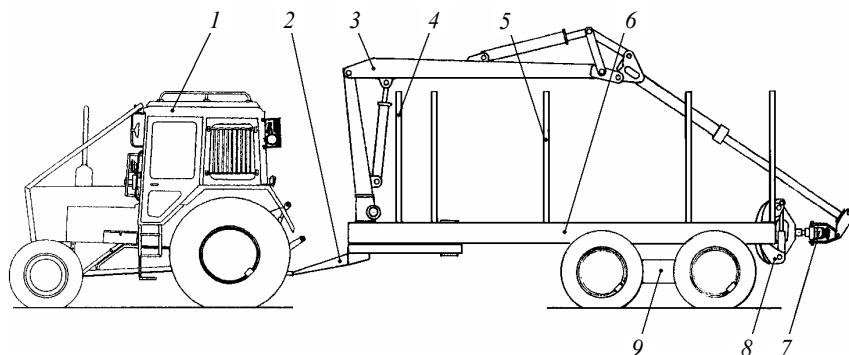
Двухзвенная погрузочно-транспортная машина «Амкодор 2652»: 1 – трактор; 2 – поворотное дышло; 3 – гидроманипулятор; 4 – щит; 5 – стойки коников; 6 – полуприцеп; 7 – ротатор; 8 – грейферный захват; 9 – балансир
